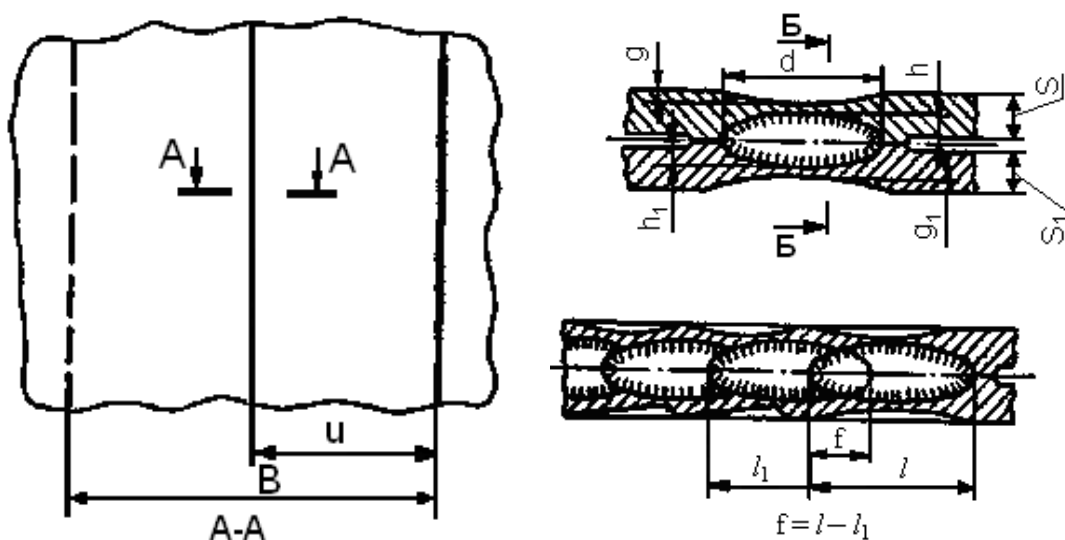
Конструктивные элементы сварных соединений, выполненных шовной сваркой
